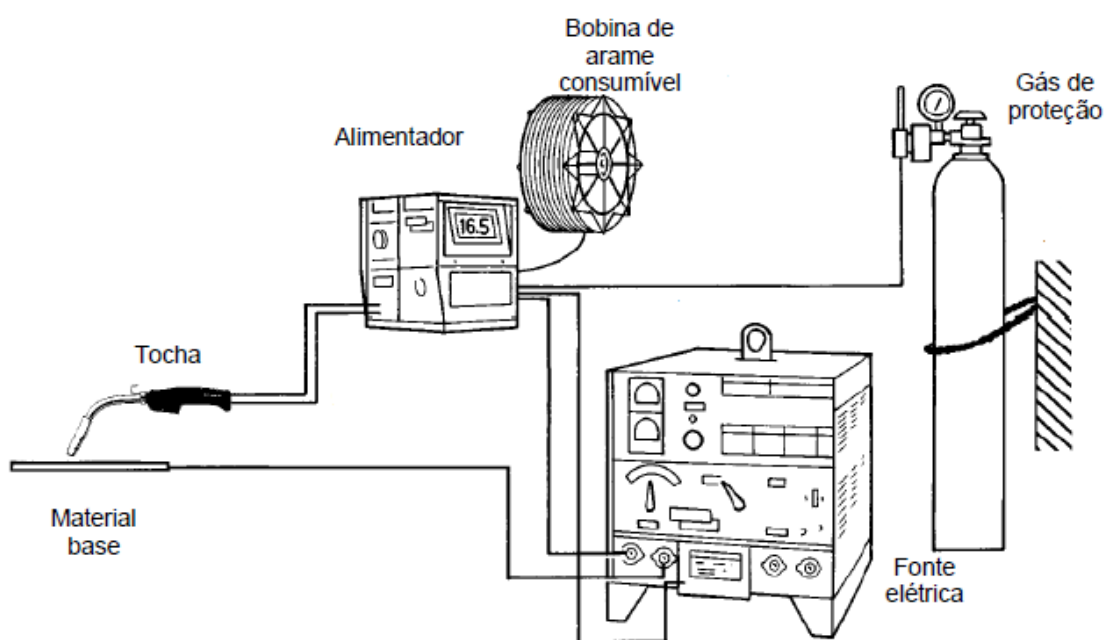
Esquema de máquina de soldar GMAW (fonte: migweldhowto).
